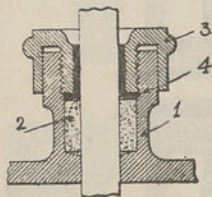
BUCINS DE PEQUENAS DIMENSÕES
